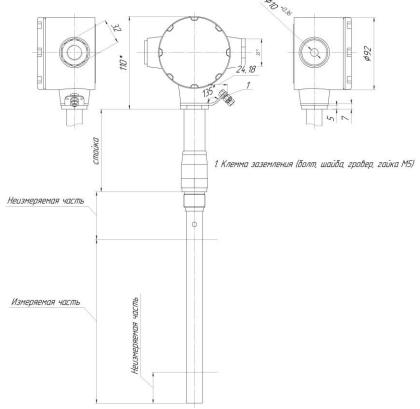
Внешний вид прибора с коаксиальным сенсором.
